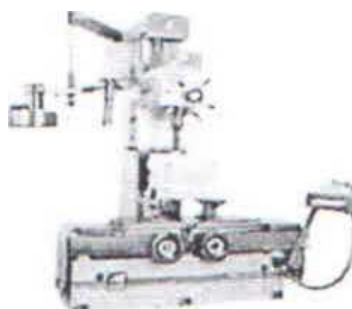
Станок для расточки и фрезеровки блоков цилиндров
